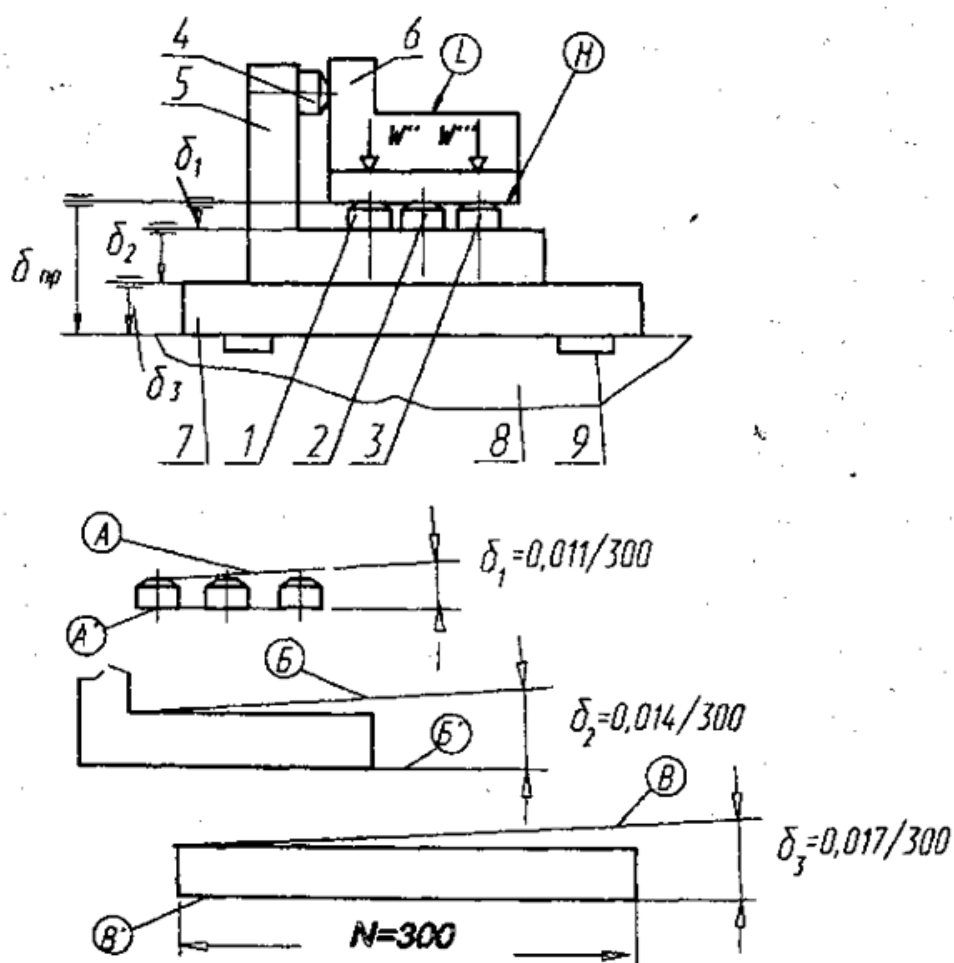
Схема размерной цепи для расчета приспособления на точность по обеспечению параллельности поверхностей L и H.
